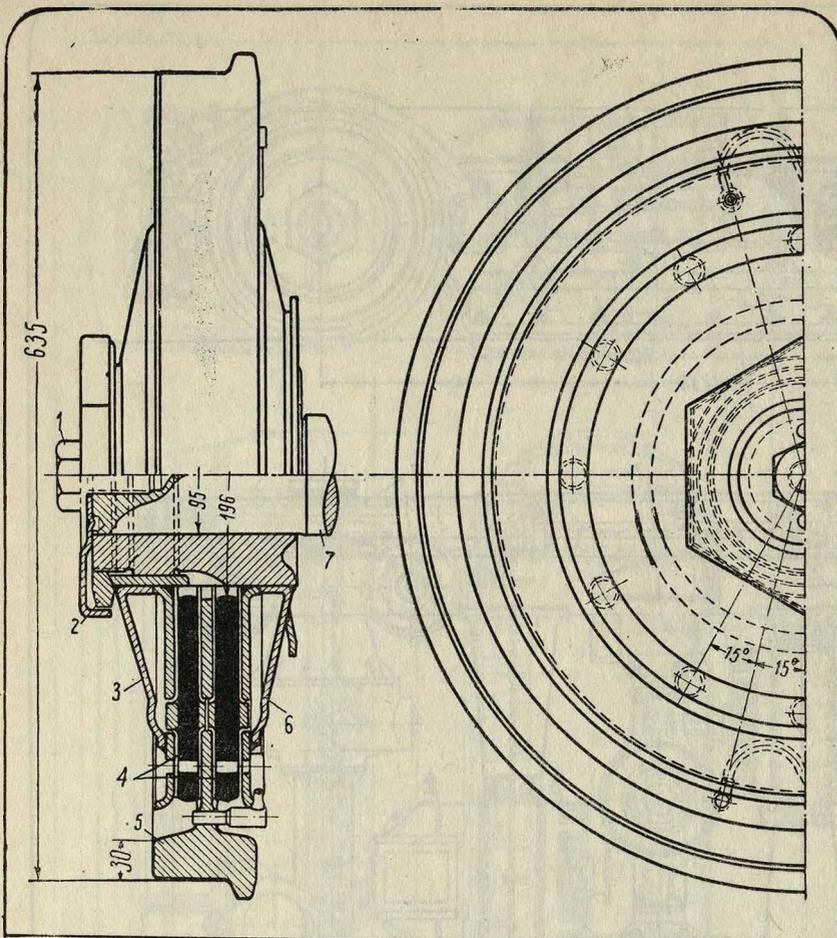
Конструкция колеса нового трамвайного вагона: 1—нажимной болт, 2—гайка, 3—нажимная шайба, 4—резиновые кольца, 5—бандаж облегченного профиля, 6—опорная шайба, 7—ось колесной пары.
